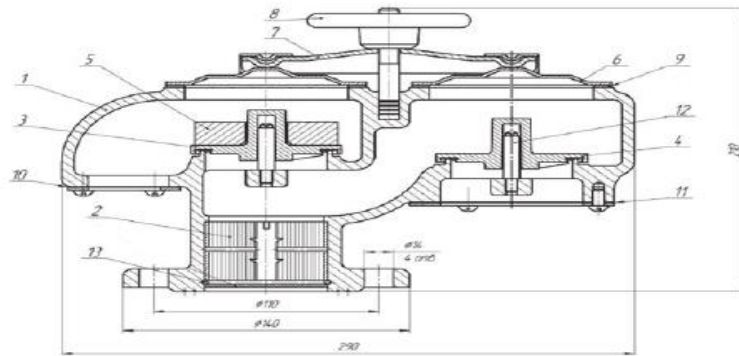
Продольний розріз клапана СМДК-50: 1 - корпус; 2 – вогневий запобіжник; 3 – тарілка тиску; 4 - тарілка вакууму; 5 - груз; 6 -кришка; 7 - ричаг; 8 - маховик; 9 - прокладки; 10, 11 - захисна сітка; 12 - направляючі осі
